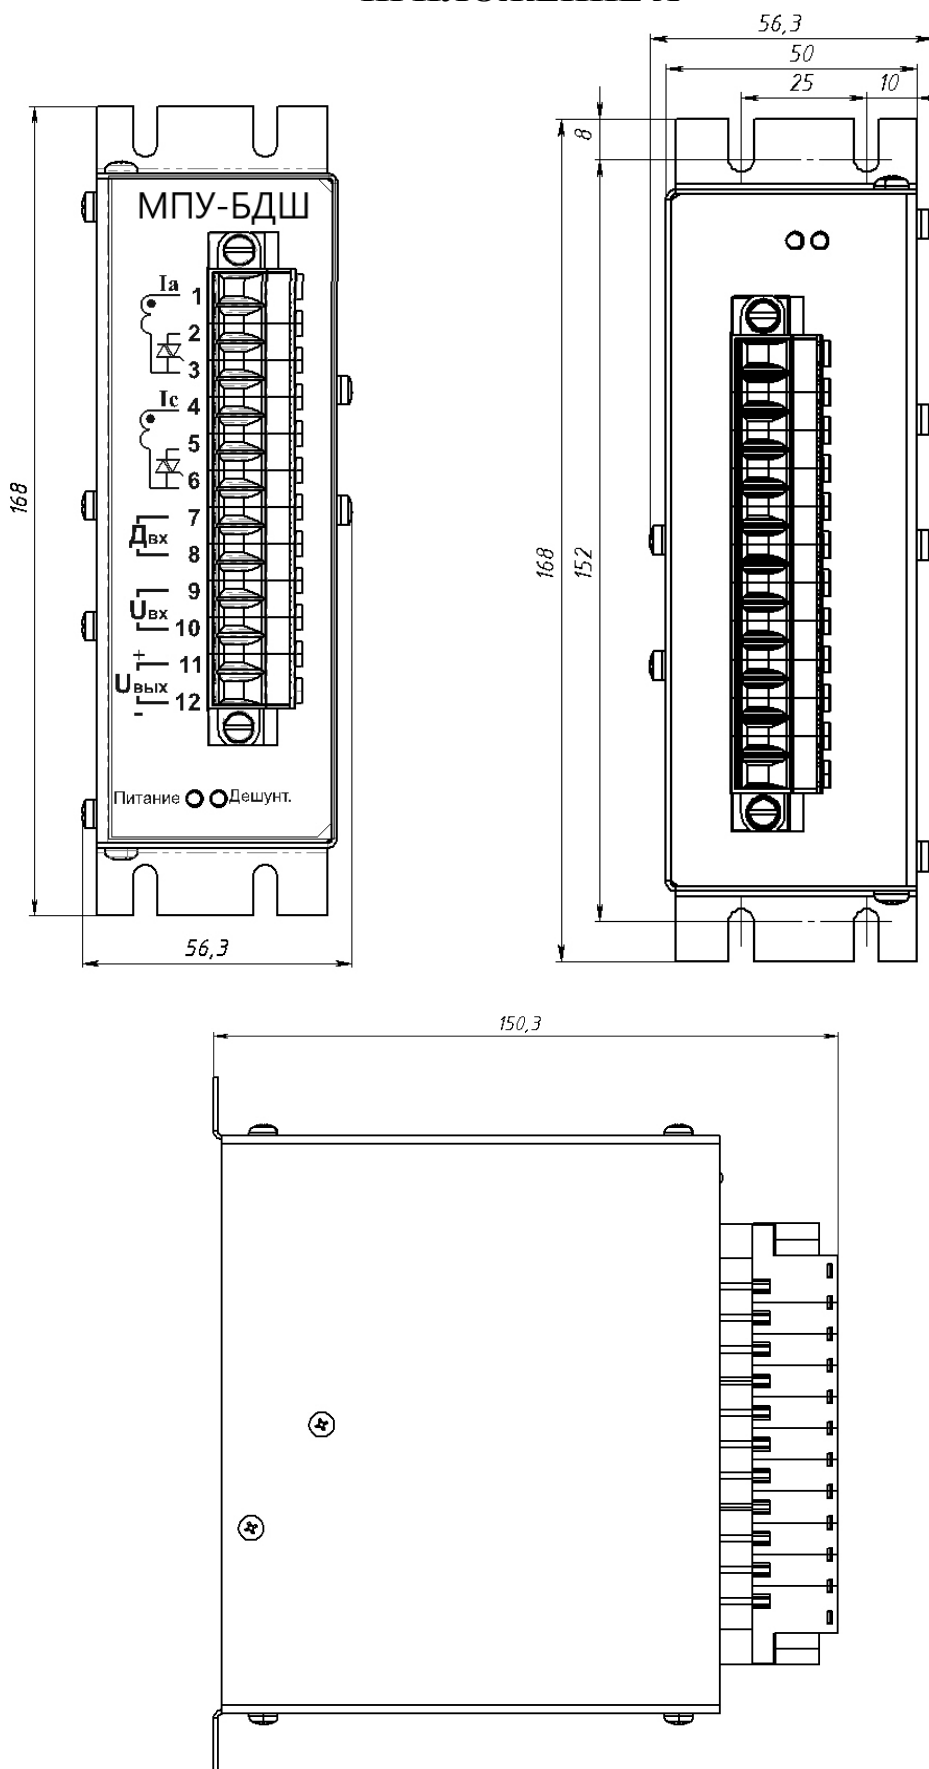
Габаритные и присоединительные размеры МПУ-БДШ
